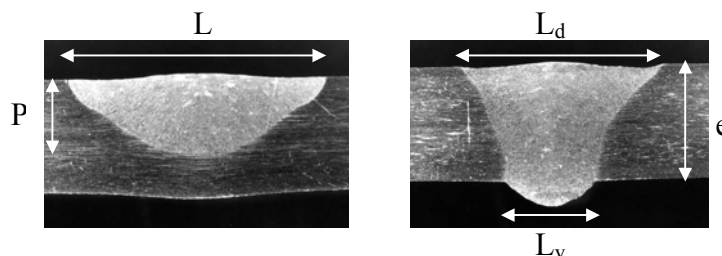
Critères d'efficacité de la soudure - soudure inox TIG (gauche) et ATIG (droite) [Sou 5]
